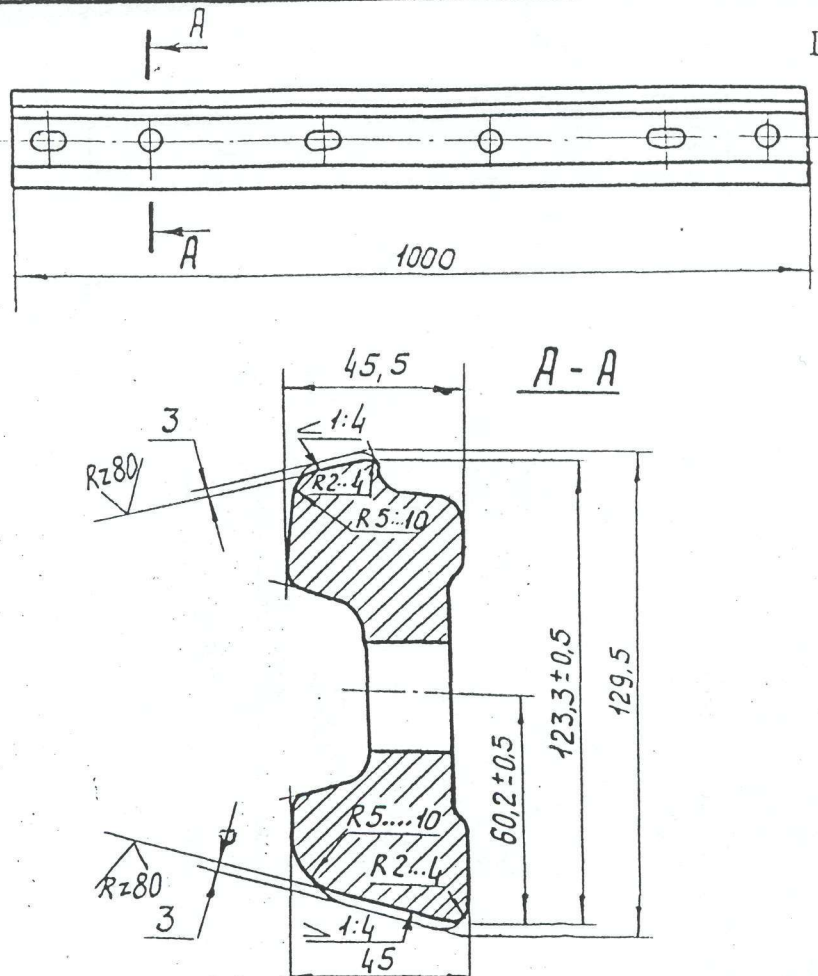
Накладка двухеоловая шестигырная типа Р65 (чертеж ОП134-71)
